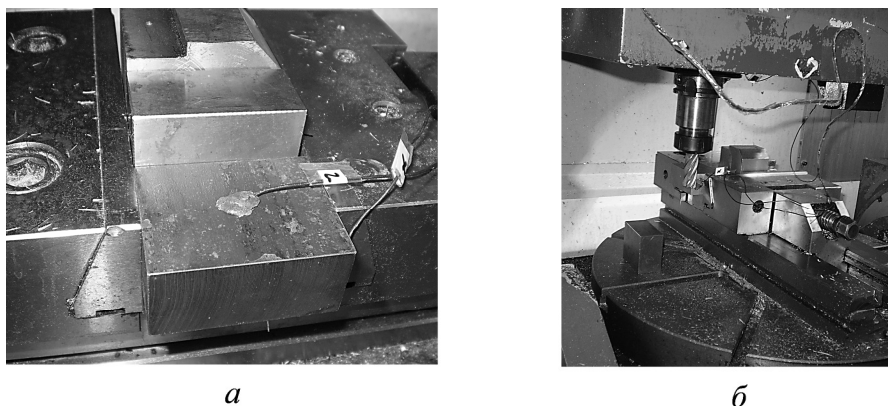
Установка призматического образца в тисках с закрепленными на нём датчиками виброускорення AP 2019 (а) и технологическая наладка для станка мод. 500V/5 (б).
